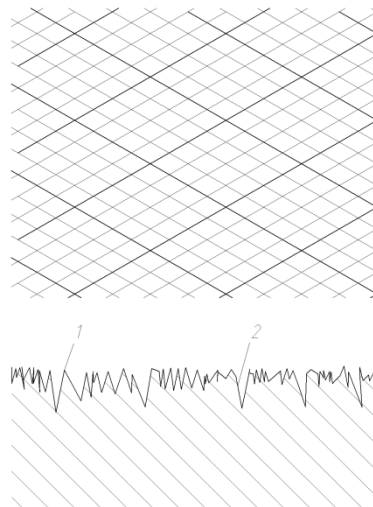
Схема робочої поверхні гільзи циліндра після плосковершинного хонінгування:
